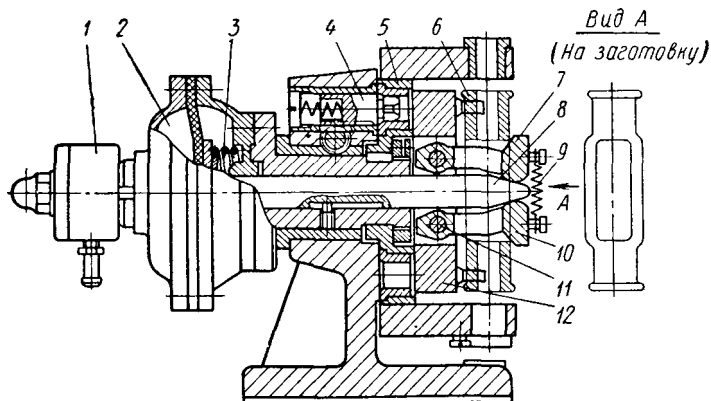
Поворотное приспособление с пневмоприводом для обработки отверстий в стяжках на вертикально-сверлильных станках
